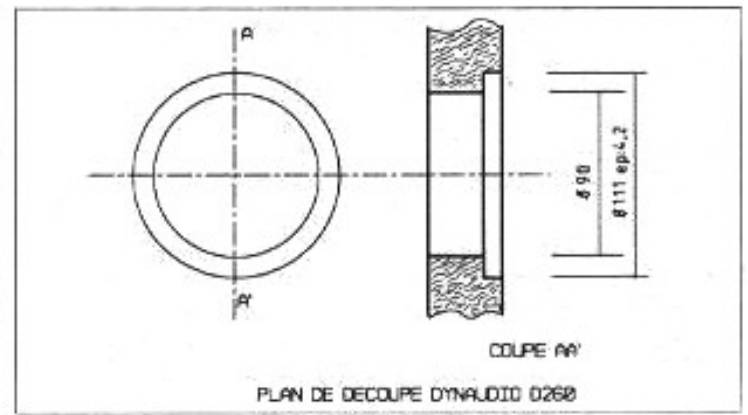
Plan de découpe de la façade avant pour le tweeter Dynaudio D 260.
